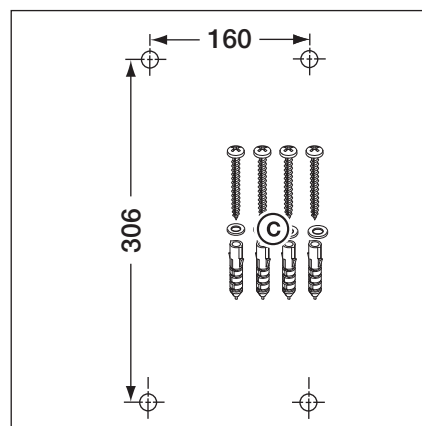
Схема расположения отверстий для крепления, необходимые детали для монтажа
